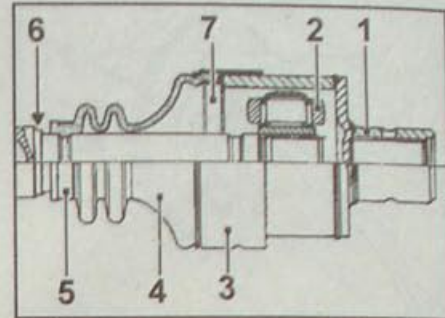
Внутренний шарнир правого приводного вала RC 490:
